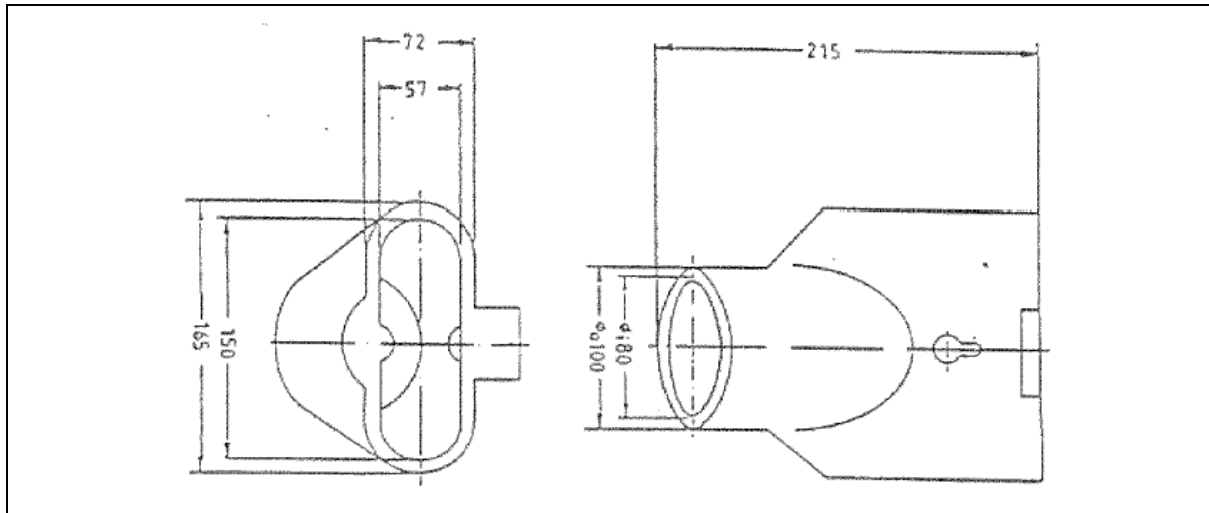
Universalauspufftülle für Schlauch DN 75
